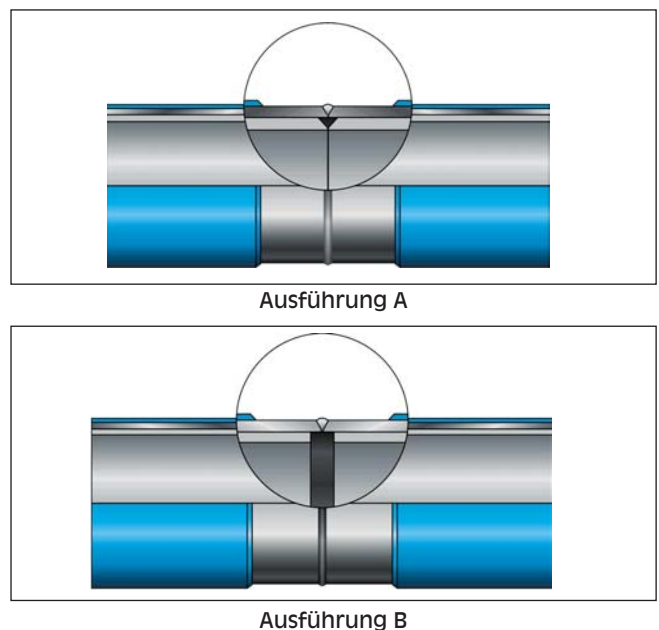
Stumpfschweißverbindungen nicht begehbaren Rohrdimensionen
